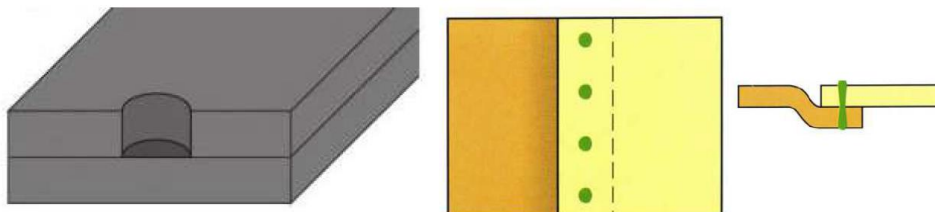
Ejemplo soldadura puntos a tapón.
